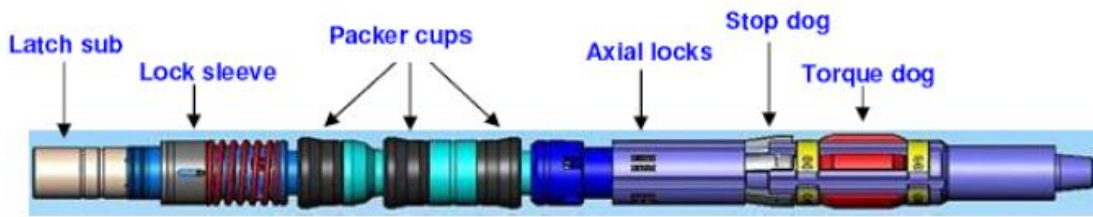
Componentes del "Drill Lock Assembly™" (SPE-134586).
